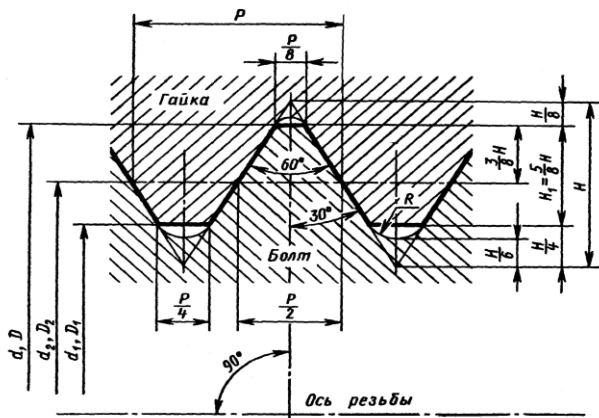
Профиль метрической резьбы по ГОСТ 9150-2002
